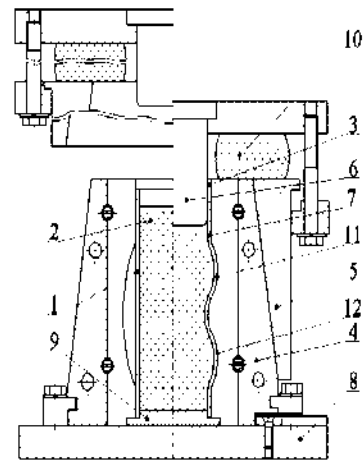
Схема процесса штамповки патрубков раздачей эластичными средами:
